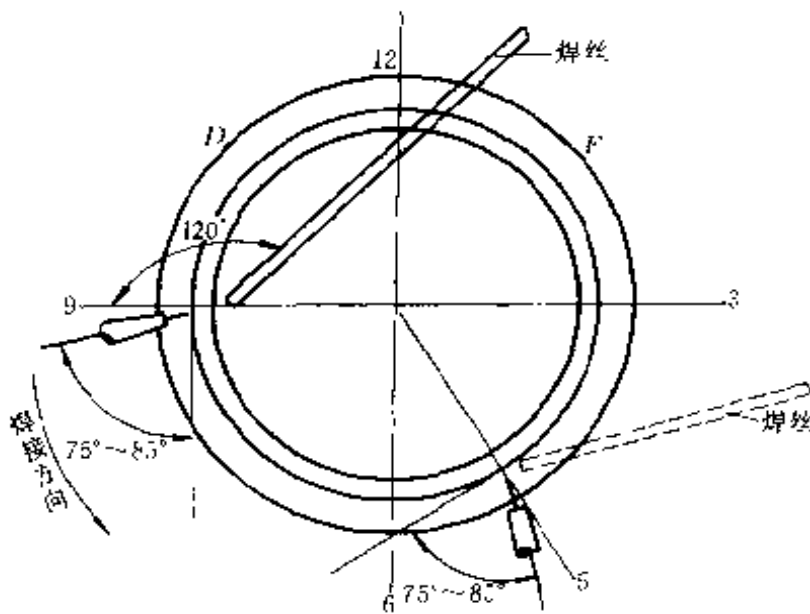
小管水平固定对接时钟 9 点位置至 6 点位置焊缝的手工 TIG 焊
